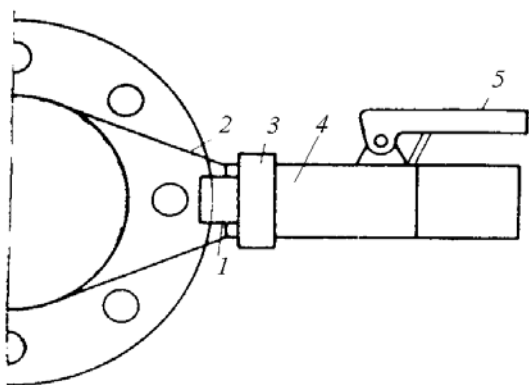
Гидравлическое приспособление для раздвижки фланцев:
